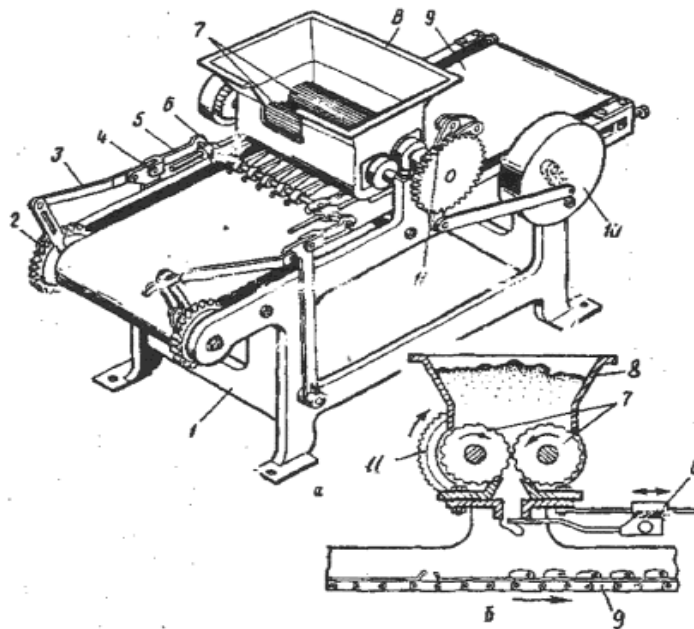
Валкова осадочна машина ФПЛ-1: а) – загальний вигляд; б) – схема формування виробів і укладання їх на конвеєр: 1 – станина; 2, 11 – храповий механізм; 3, 4, 5 – важіль; 6 – струнотримач; 7 – валок; 8 – воронка; 9 – конвеєр; 10 – маховик.
